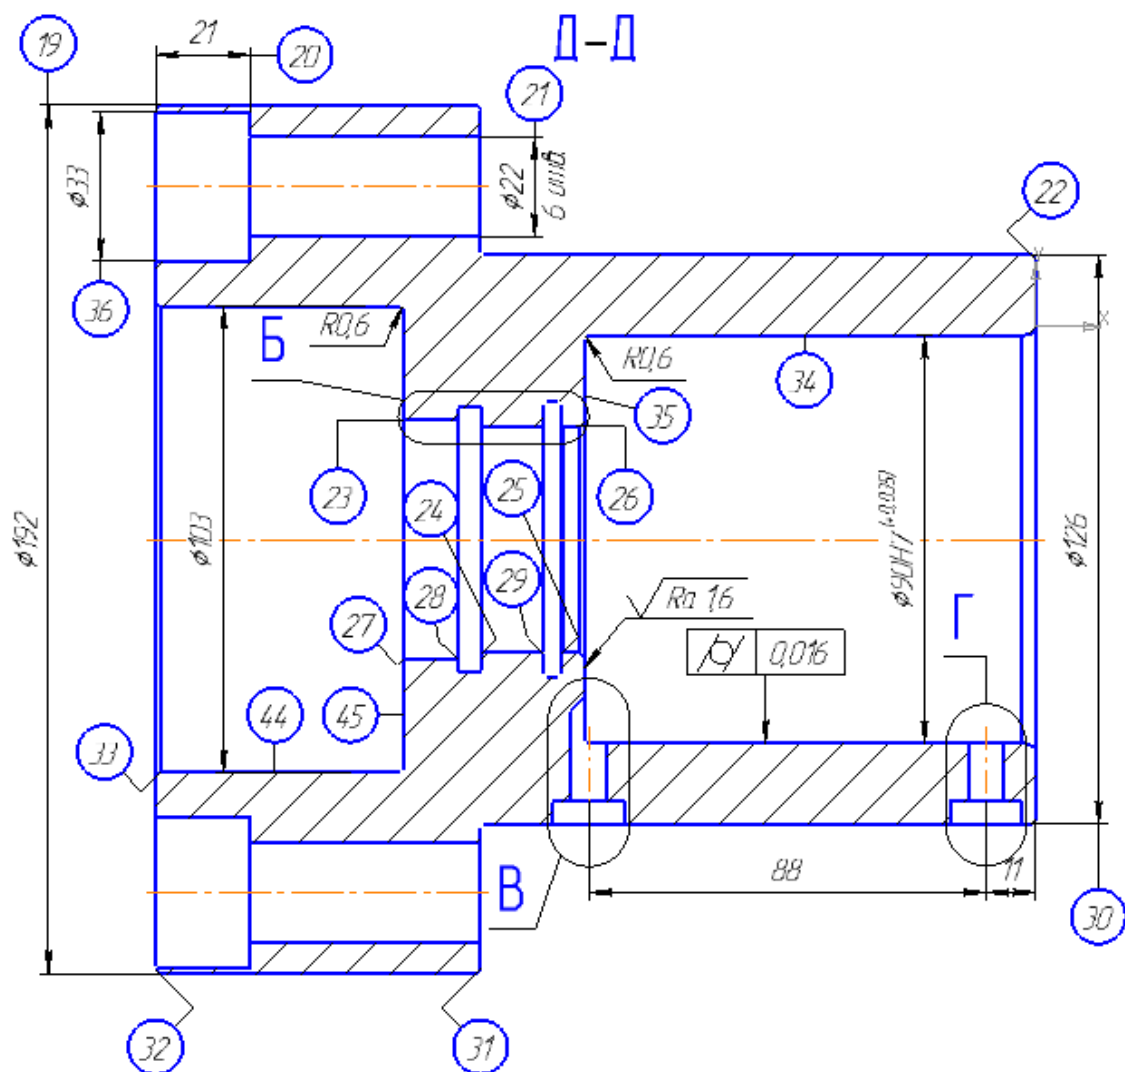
Эскиз детали «Корпус гидроцилиндра шиберного затвора»
